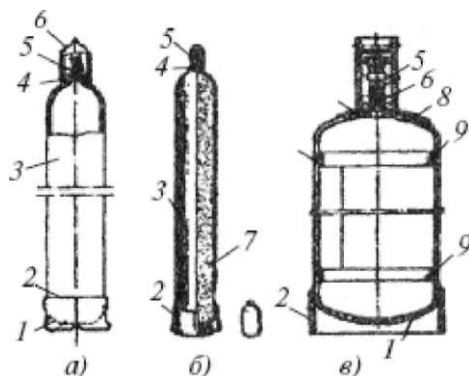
Баллоны для сжатых газов: а - кислородный; б - ацетиленовый; в - (сварной) для пропан-бутана; 1 - днище; 2 - башмак опорный; 3 - корпус; 4 - горловина; 5- вентиль; 6 - колпак; 7 - пористая масса; 8 - паспортная табличка; 9 - подкладные кольца
